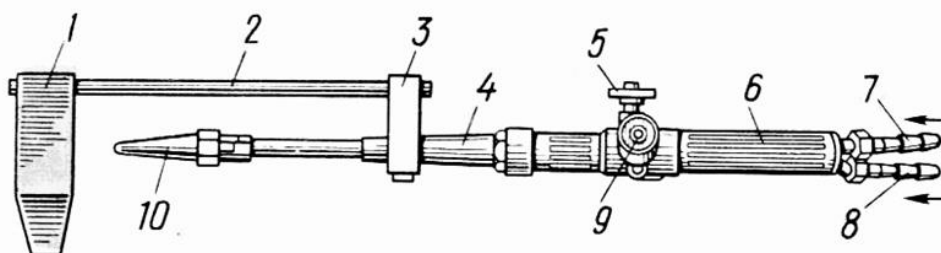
Конструкция газового паяльника: 1 – рабочая часть; 2 – стержень металлический; 3 – хомут; 4 – камера смесительная; 5 и 9 – вентили регулировочные для подачи кислорода и газа; 6 – рукоятка; 7 и 8 – ниппели для кислорода и газа; 10 – сопло
